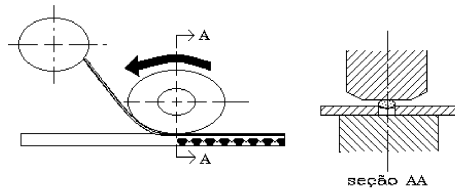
(c) - Soldagem por Costura com Tira Metálica.
